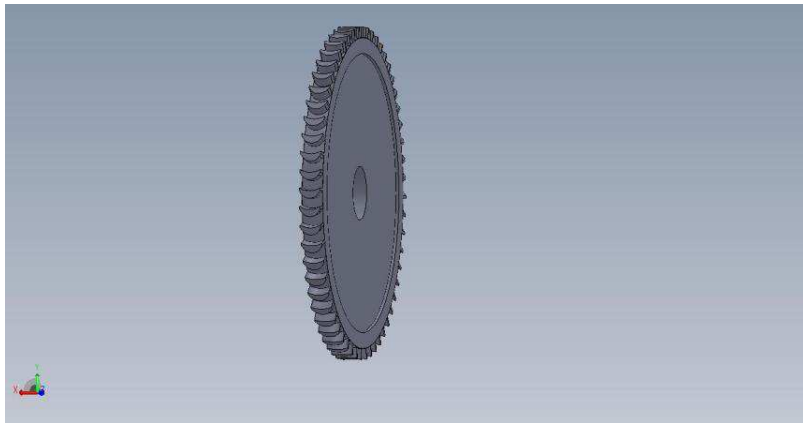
Vista en Tercera dimensión de la geometría primitiva del Rotor
